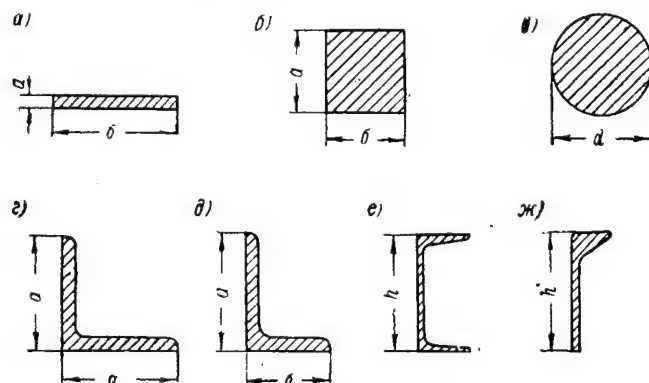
Виды сортовой и фасонной стали: а — полосовая; б — квадратная; в — круглая; г — угловая равнобокая; д — угловая неравнобокая; е — швеллерная; ж — полособульбовая.
